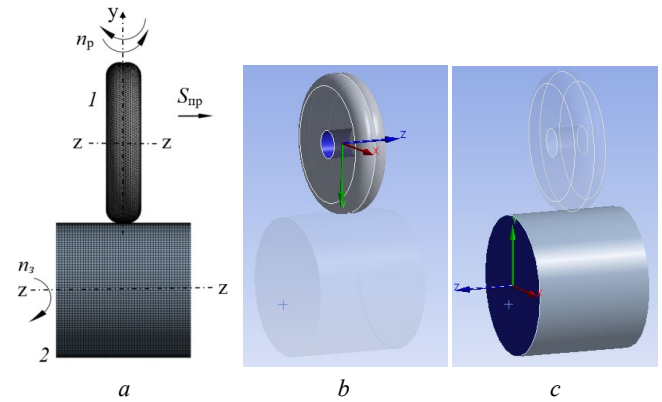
Конечно-элементная модель реверсивного ППД двухрадиусным роликом (*a*), граничные условия для рабочего инструмента (*b*) и заготовки (*c*); 1 – двухрадиусный ролик; 2 – цилиндрический образец
